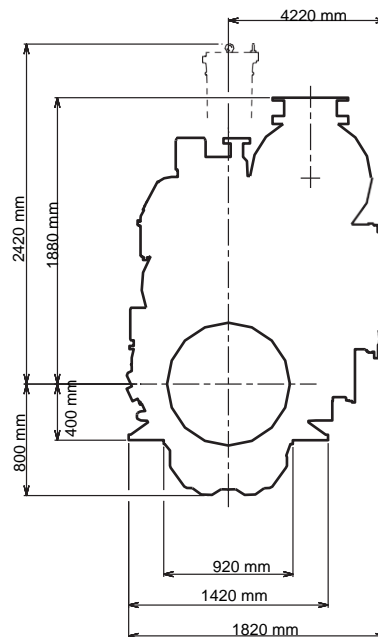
Dimensiones de vista frontal del motor Wärtsilä 6L26A. Se considera cárter seco. "Wärtsilä Marine Project Guide W26A 1/2003"
